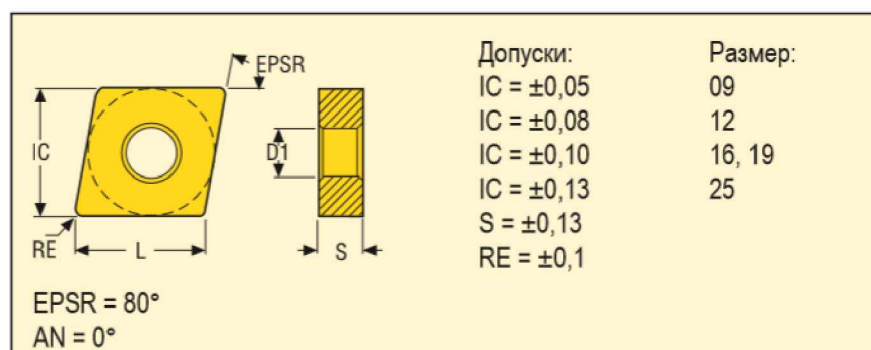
Пластина CNMG120408-MR6 з покриттям TP1500 для чорнової обробки [1, с.393]
